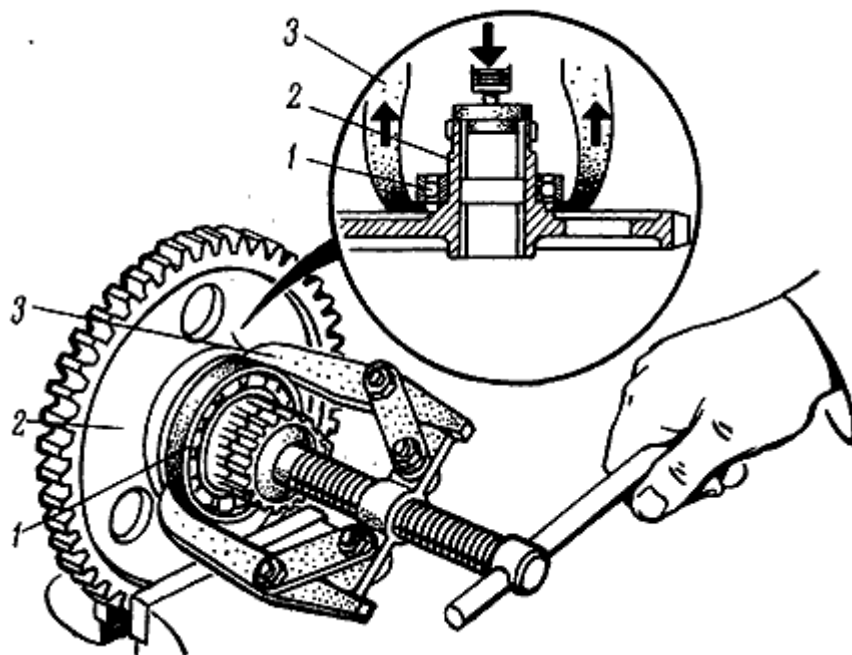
Спрессовка подшипника с шестерни I ступени привода ВОМ:
